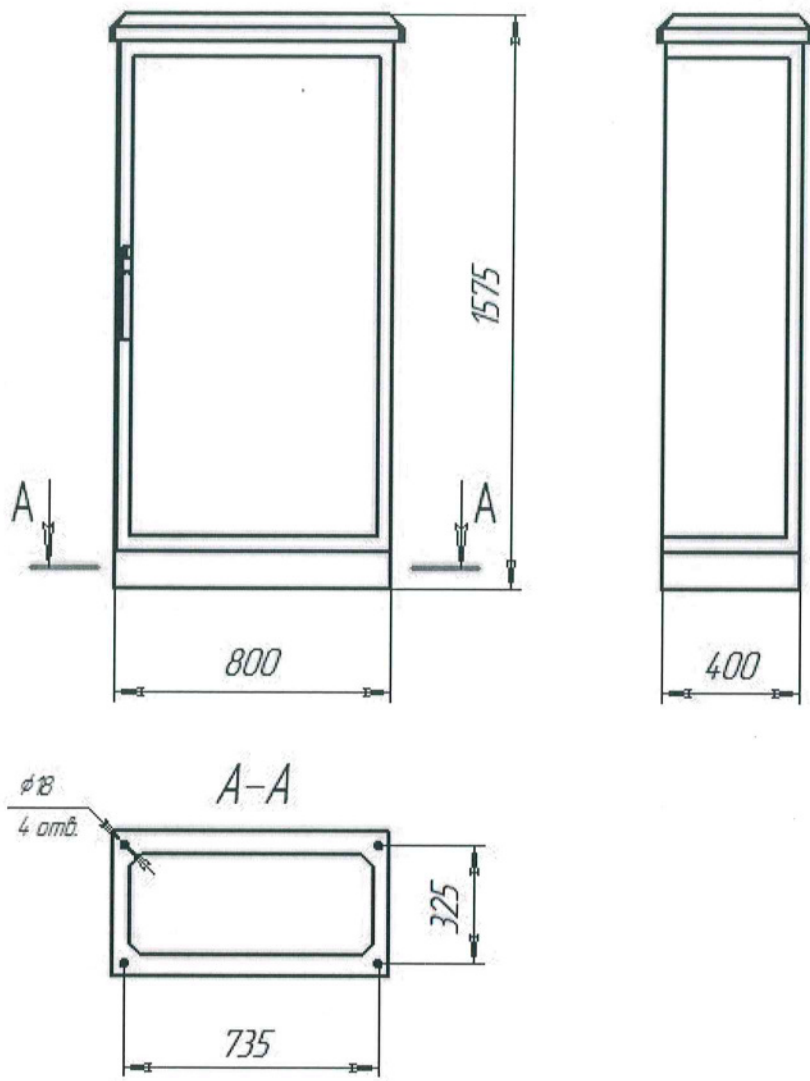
Габаритные и установочные размеры шкафа высотой Н=1575 мм
